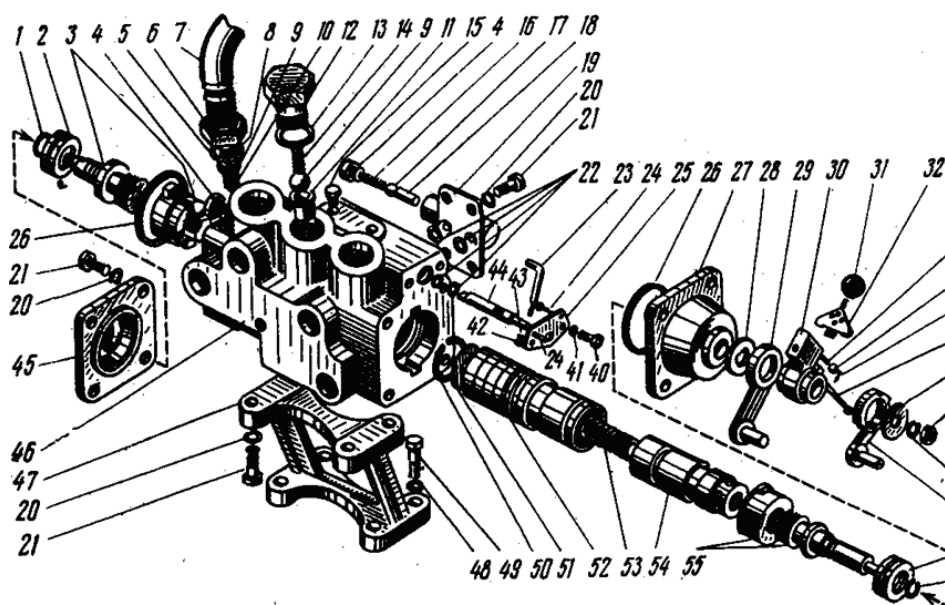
Разборка силового регулятора. 1, 5, 13 и 32 — уплотнительные кольца; 2 — подшипник; 3 — винт гильзы; 4 и 15 — пробки; 6, 36 и 42 — гайки; 7 — поворотный штуцер; 8, 16 и 53 — пружины; 9, 17 и 34 — шарики; 10 — толкатель; 11 — седло обратного клапана; 12 — корпус с клапана; 14 — пружина всасывающего клапана; 18 — седло клапана; 19 — клапан в сборе; 20, 28, 37, 41, 43 и 48 — шайбы; 21, 40 и 49 — болты; 23 — рычажок крана; 24 — упор; 25 — фланец крана; 26 — уплотнительное кольцо упора; 27 — правая крышка; 23 — позиционный рычаг золотника; 30 — муфта; 31 — ручка; 32 — фиксатор; 33 — пружина обгонной муфты; 35 — шплинт; 38 — силовой рычаг золотника; 39 — ось фиксатора; 40 — кран; 45 — левая крышка; 46 — корпус с регулятора; 47 — кронштейн; 50 — кольцо; 51 — шайба пружины; 52 — гильза; 54 — золотник; 55 — винт золотника
